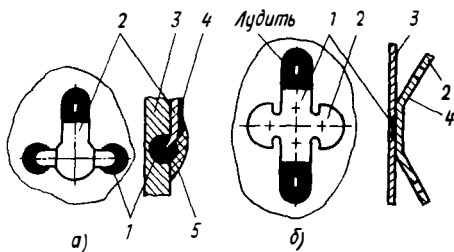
Соединение сваркой контактного лепестка из плакированного медью алюминия с корпусом из алюминиевого сплава с помощью аргодуговой сварки (а) и точечной электросварки (б):
